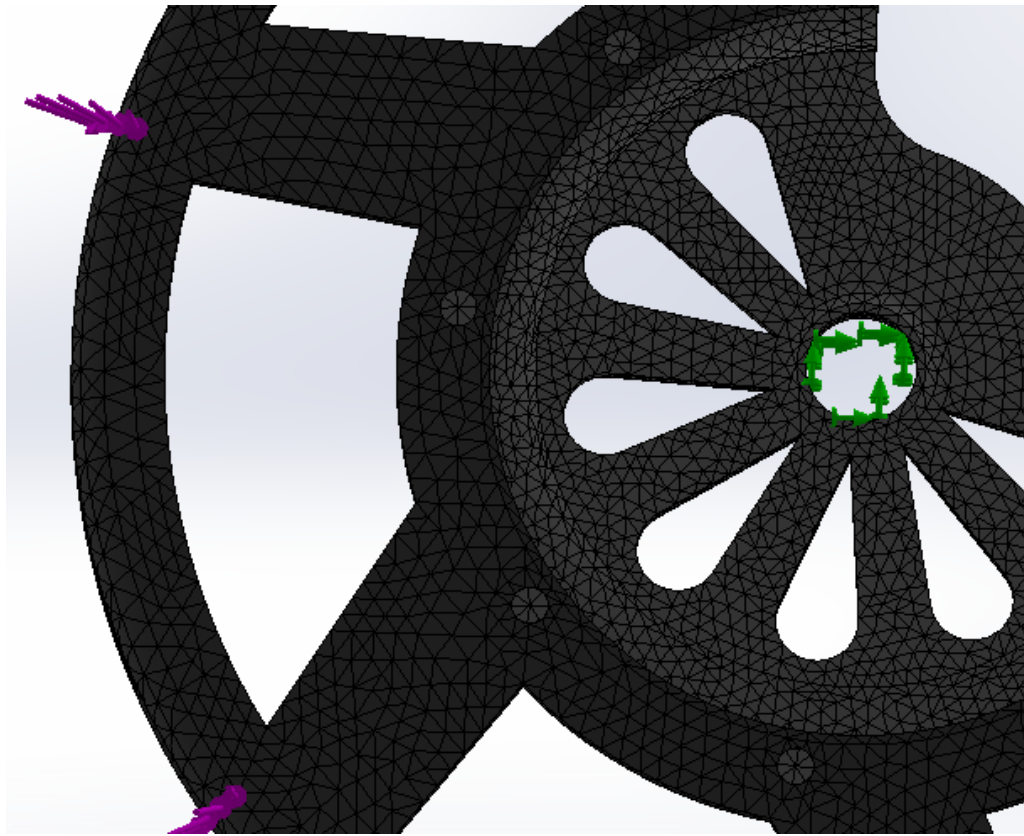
Vista del mallado, la fijación del conjunto y la aplicación de la fuerza en el ensayo.
